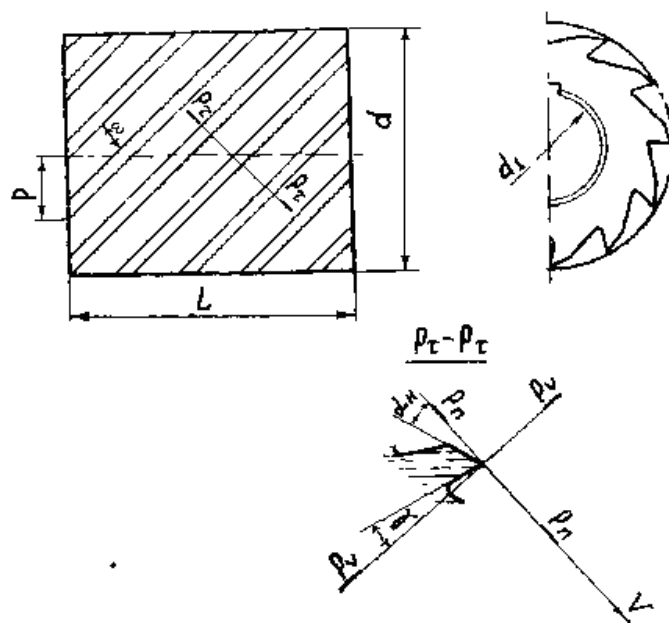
Элементы и геометрия цилиндрической насадной фрезы
